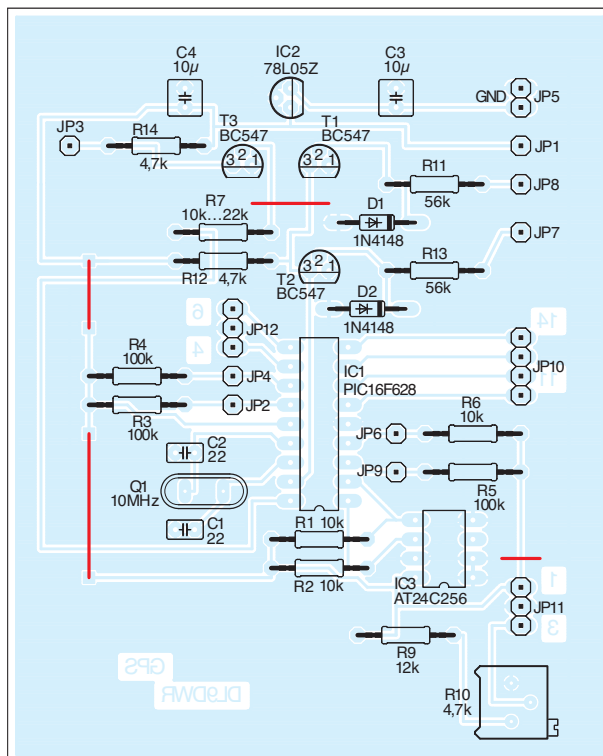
Bestückungsplan der Baugruppe; bitte nicht die vier rot markierten Brücken beim Aufbau vergessen.
